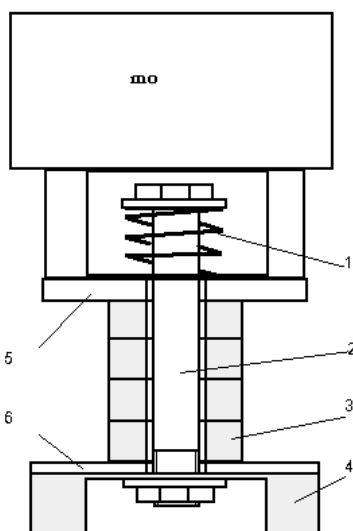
Составной пакетный пьезодвигатель с нагрузкой
